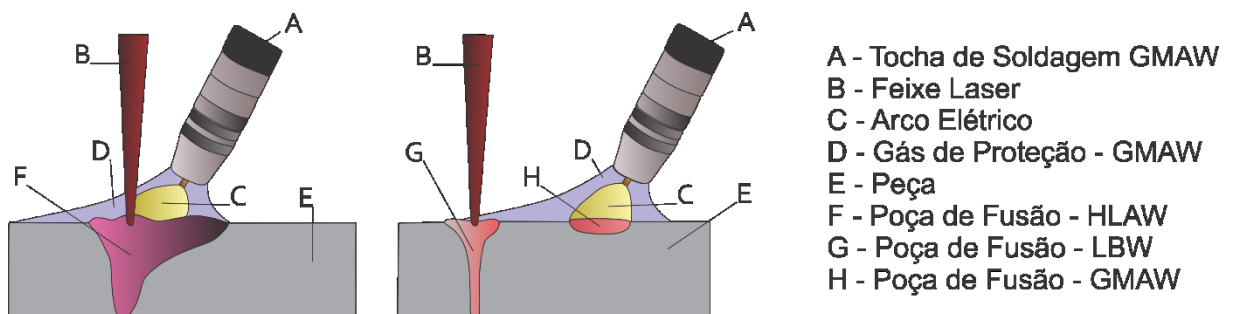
Esquemático comparativo entre os processos de soldagem híbrida (HLAW) e o soldagem assistida. (Fonte: Autor)
